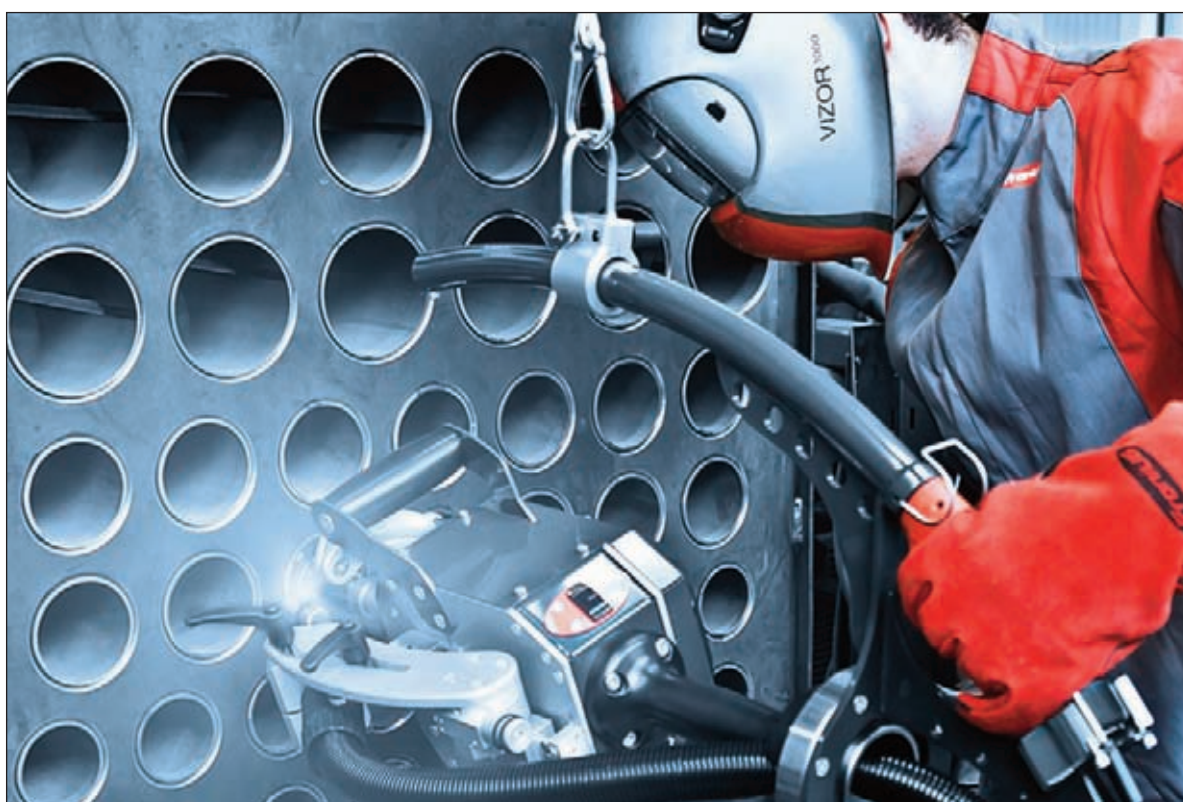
Выполнение сварных соединений типа «труба-трубная доска» в вертикальном положении заподлицо
